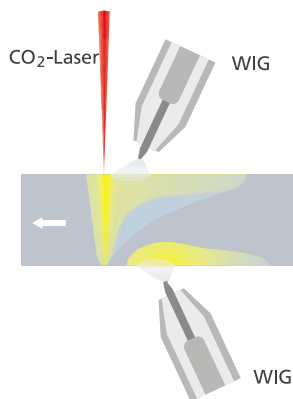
Laserstrahl-Hybridschweißen (CO₂-Laser + WIG) mit integrierter Wurzellagenschweißung
